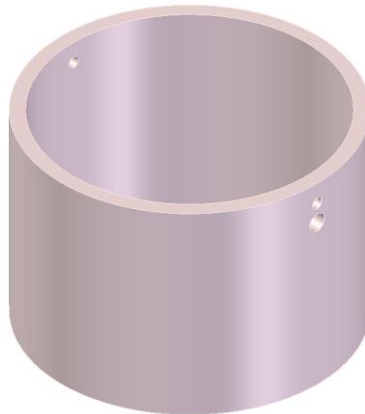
Carcasa del rebobinador de cordón para la herramienta de corte.
